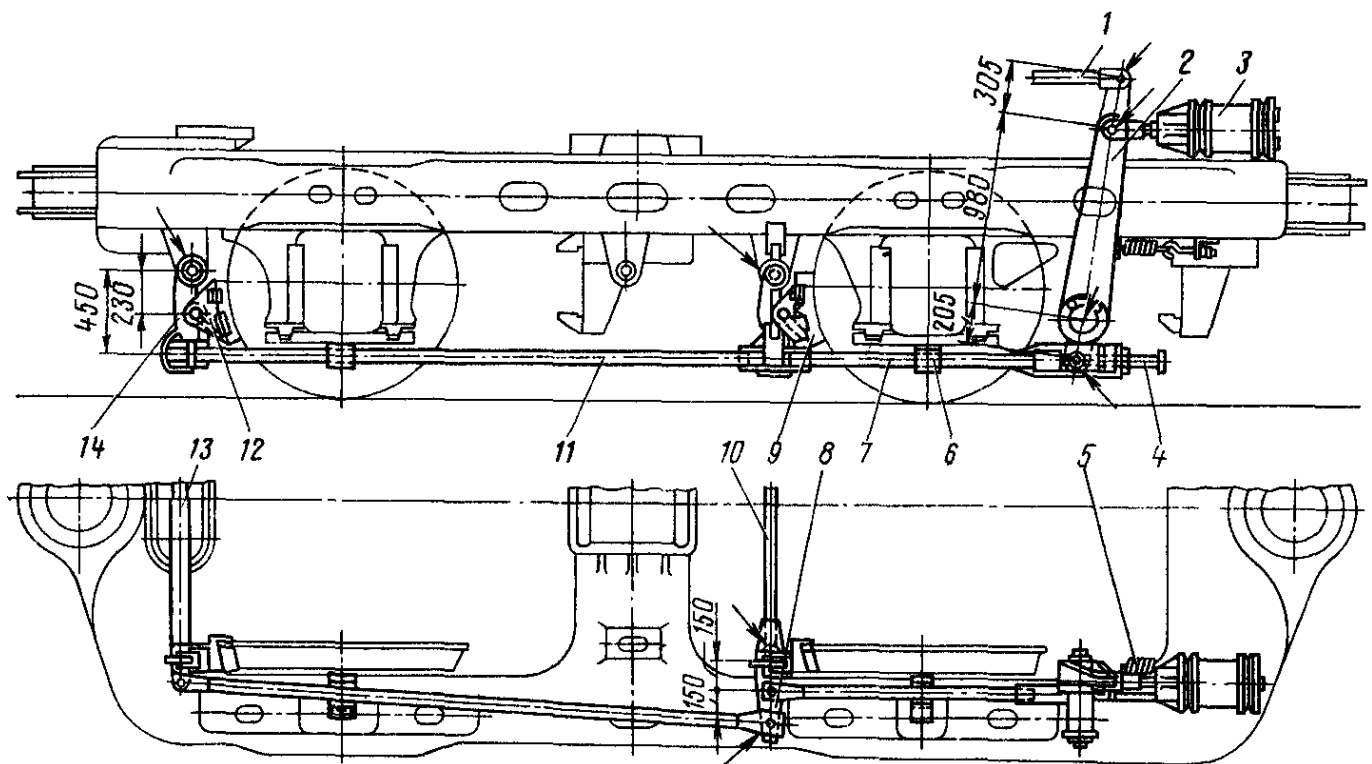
Тормозная рычажная передача (стрелками указаны места смазки)
